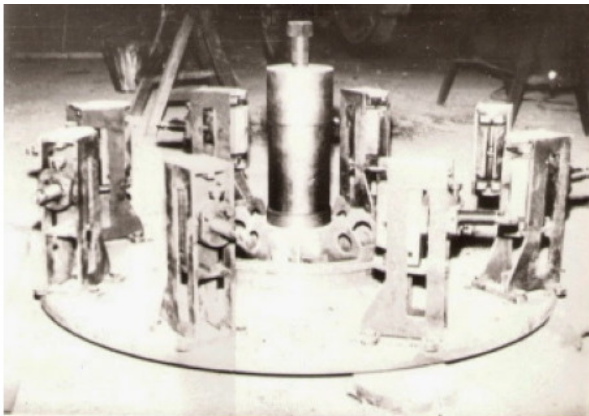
Стенд для сборки сварного рабочего колеса центробежного насоса 24НДс
